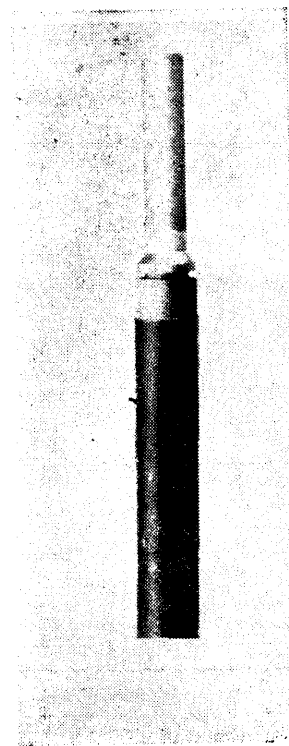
Einpressen der Lenkrohrbüchse und des Lauftringes mittels Vorrichtung D-59.
